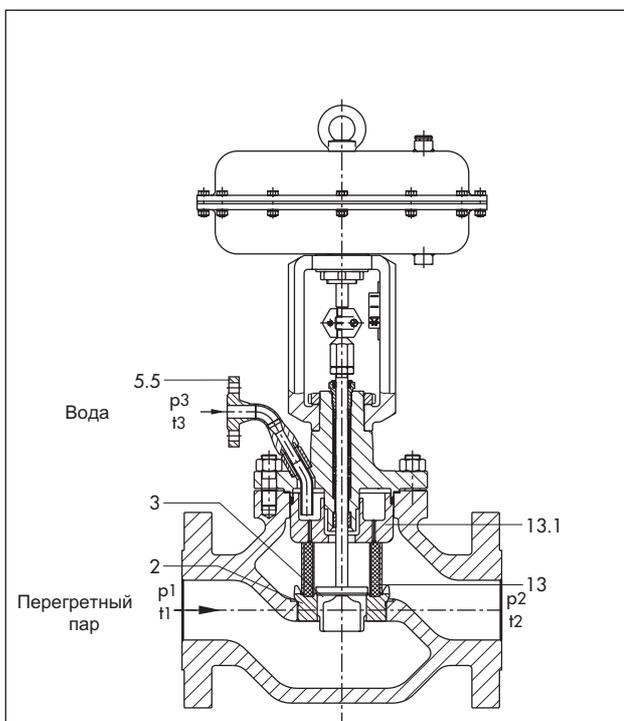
· Пневматический паропреобразователь тип 3281-1 с фланцевым соединением и исполнительным приводом тип 3271
